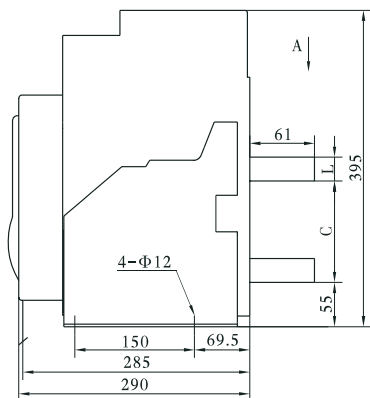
Габаритные размеры стационарных трехполюсных выключателей типоразмера D
